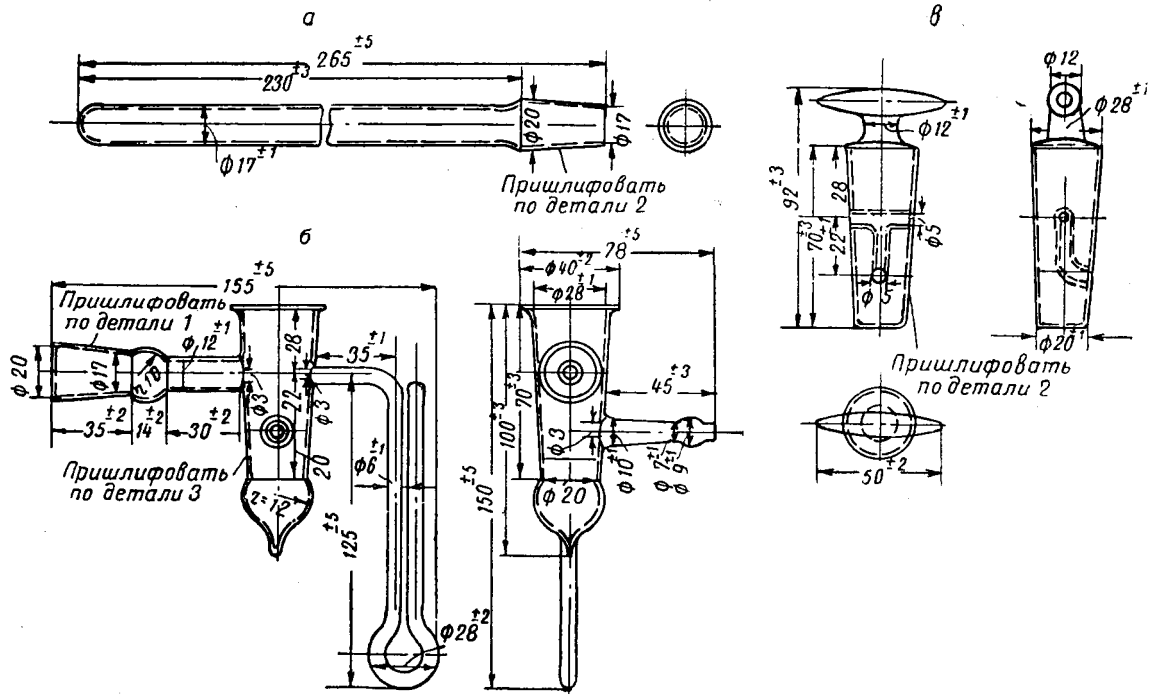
Чертежи деталей прибора форвакуумного нагрева:
